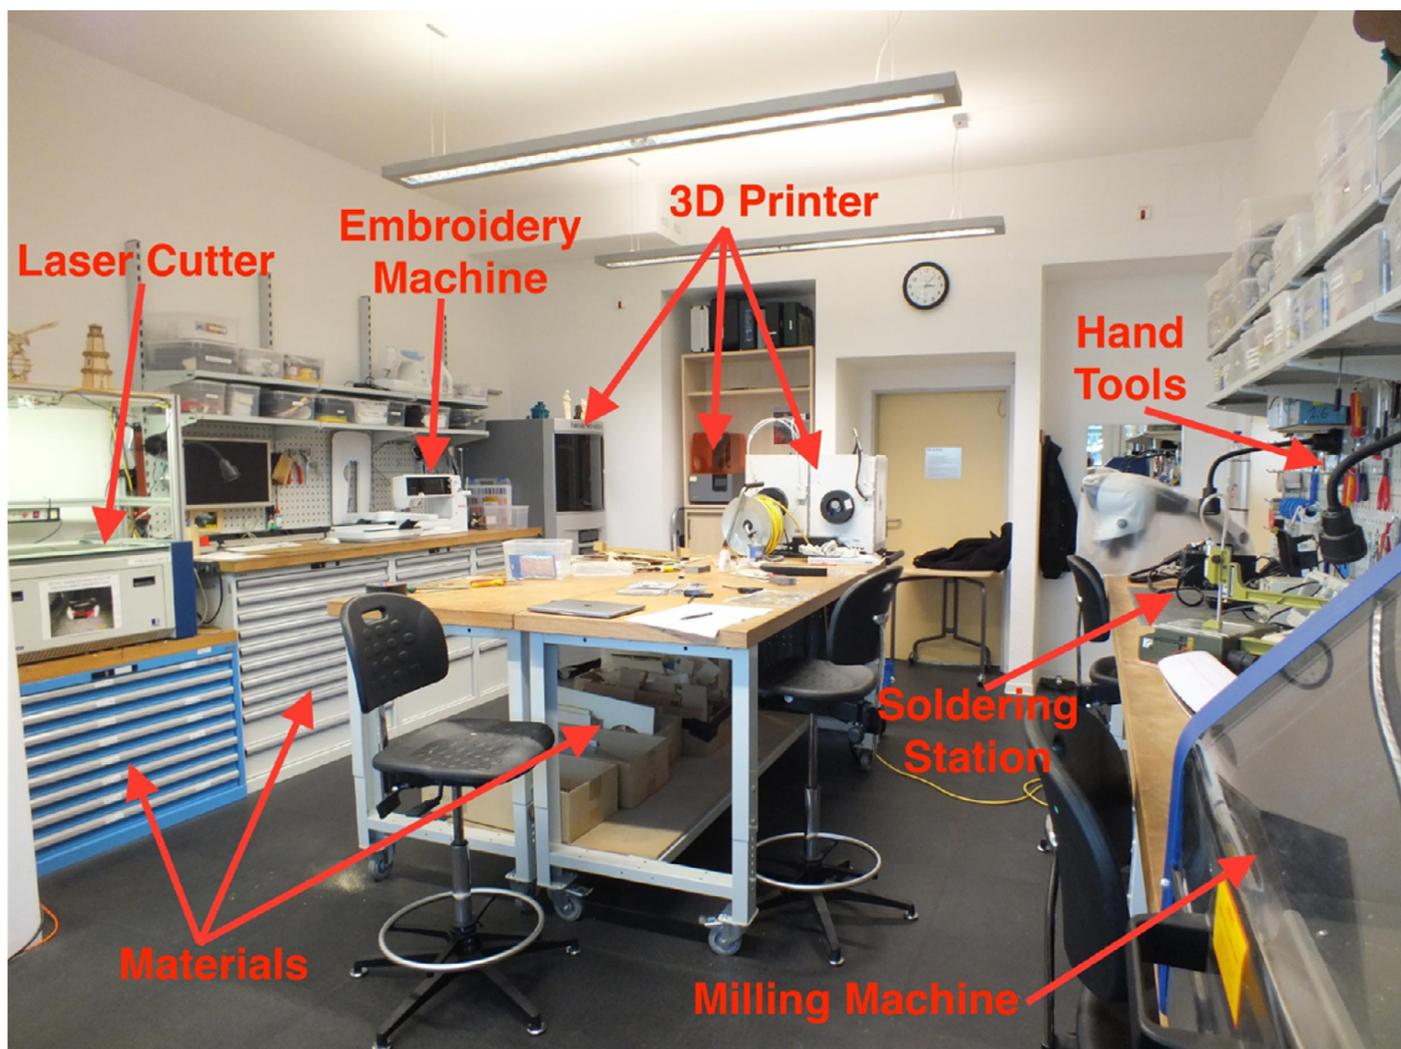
Beispielhaft der Blick in das Fab Lab der RWTH Aachen. Zu sehen sind Maschinen wie der Laser Cutter und der 3D Printer sowie klassische Werkzeuge.
